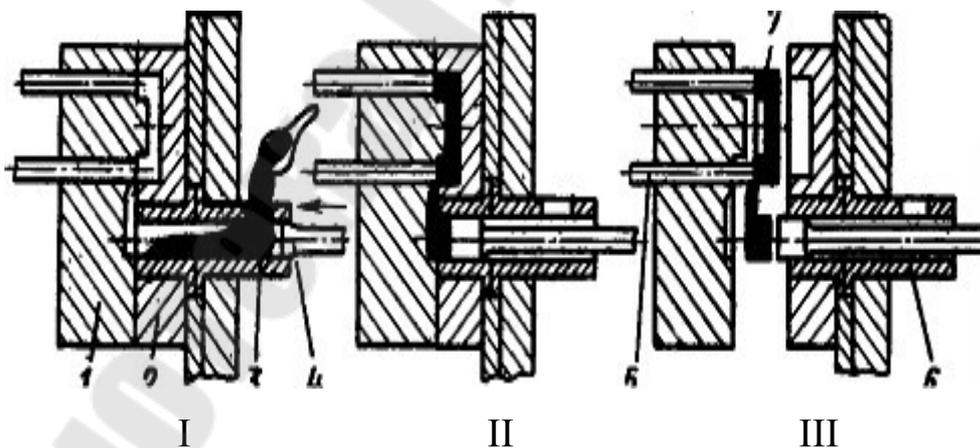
Схема технологического процесса получения отливок на машине для литья под давлением с горизонтальной холодной камерой прессования: I- заливка металла; II- запрессовка металла; III- открытие формы; 1- подвижная половина формы; 2- неподвижная половина формы; 3- жидкий металл; 4- прессовый плунжер; 5- толкатель; 6- прессовый стакан; 7- отливка.
